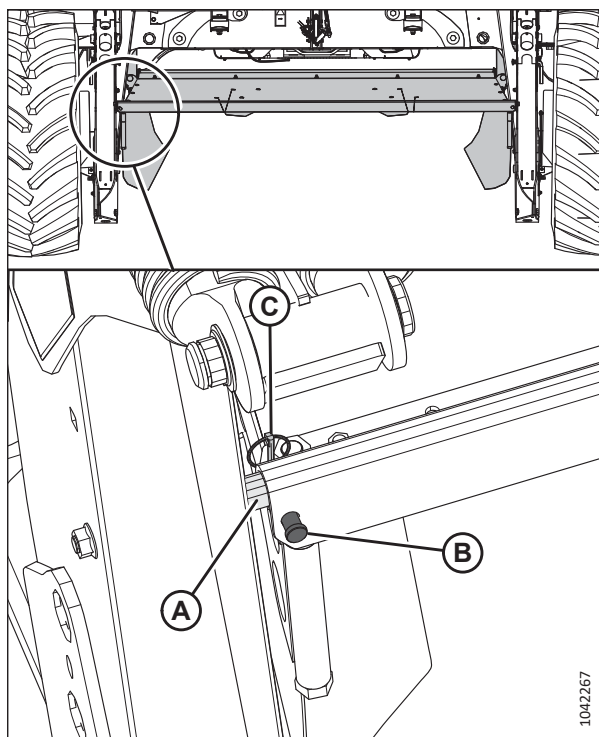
Формовочный щиток, прикрепленный к лапе косилки
